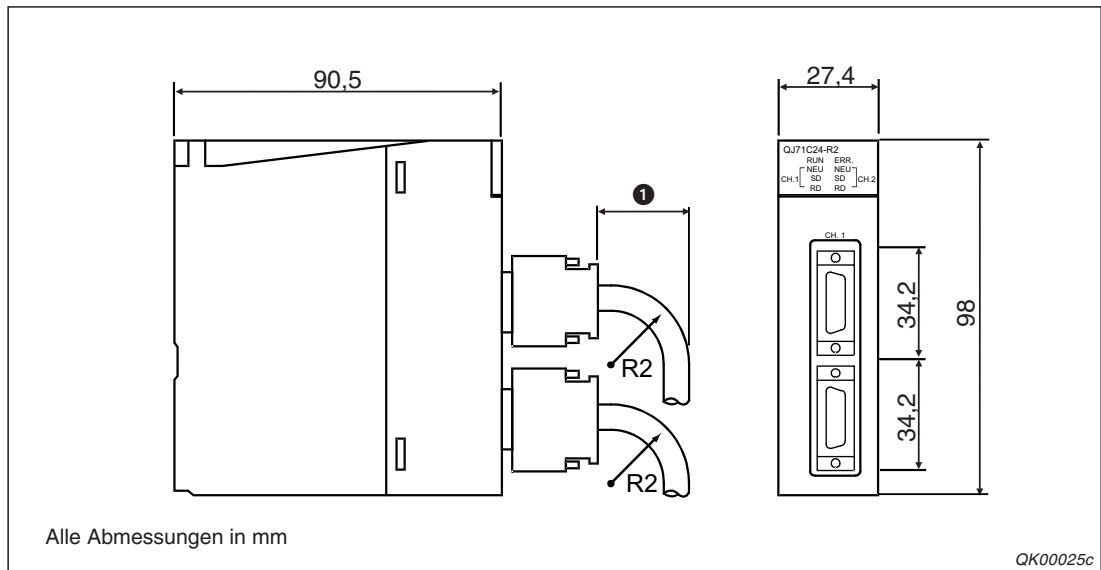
Abmessungen der Module QJ71C24-R2 und QJ71C24N-R2
